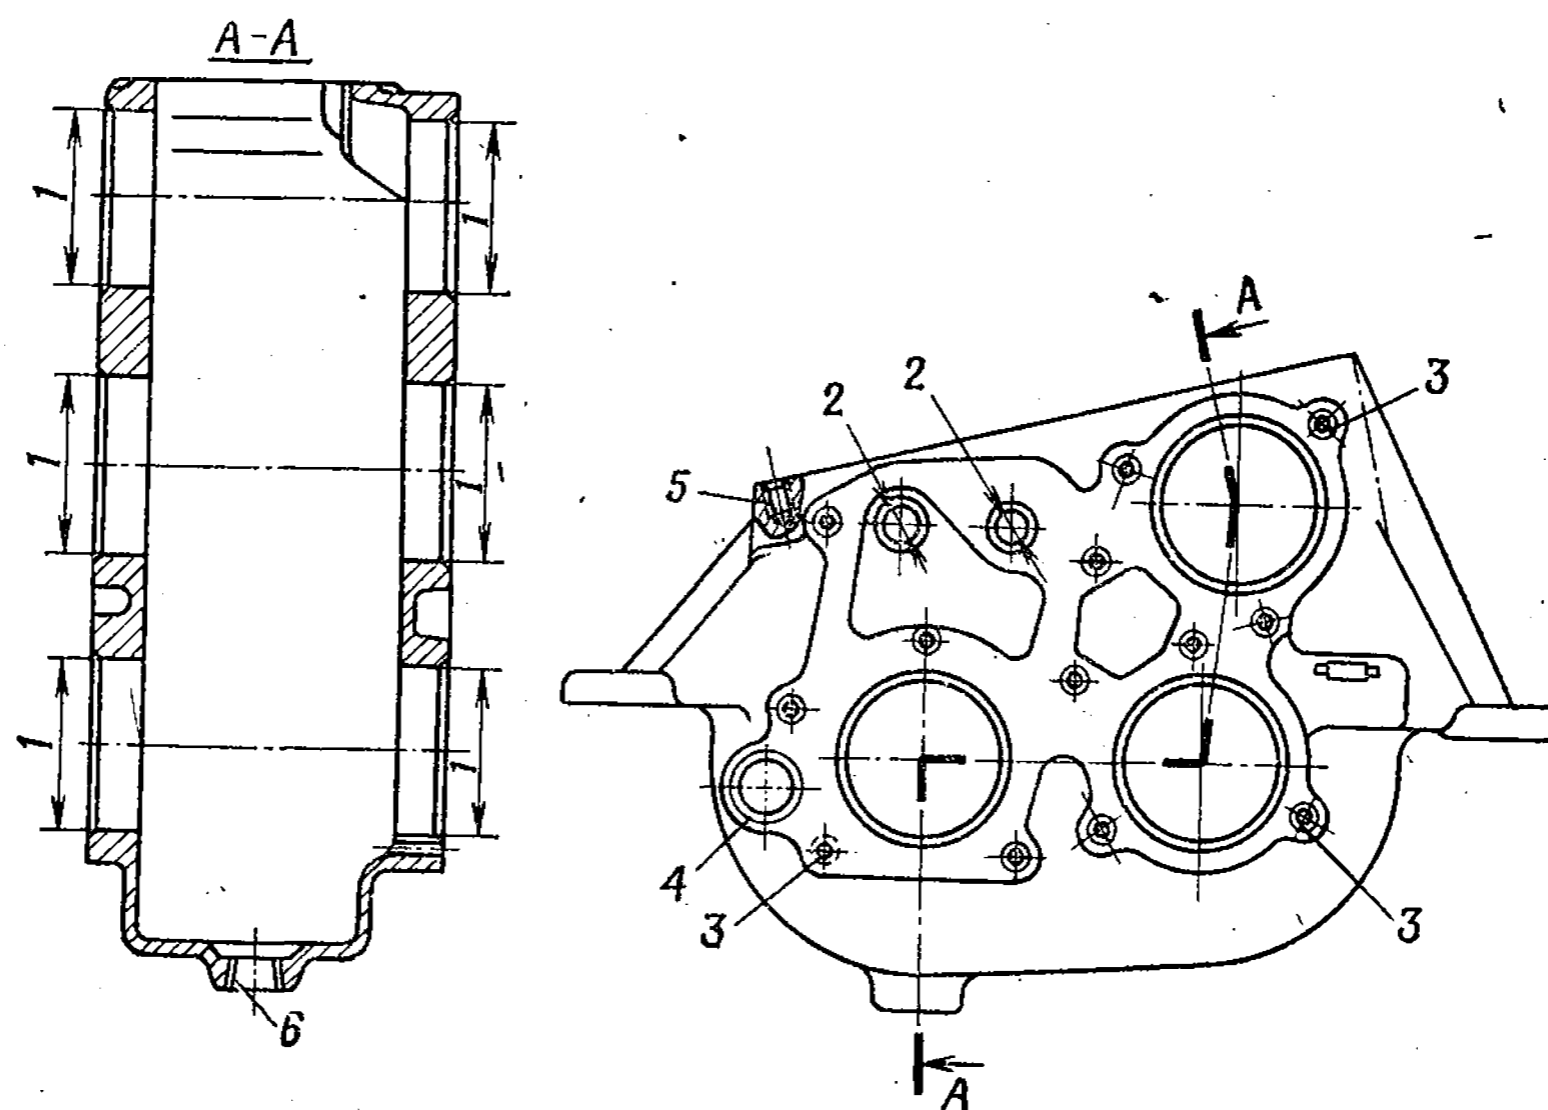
Картер раздаточной коробки с заглушкой в сборе
